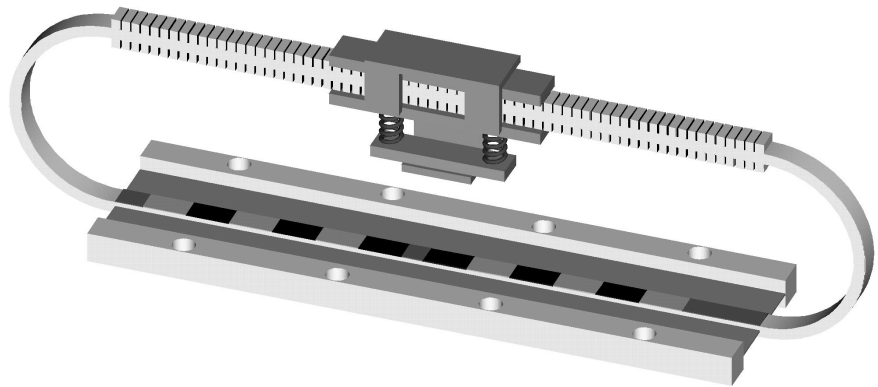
Linearer Wanderwellenmotor mit Ringstator [7]
